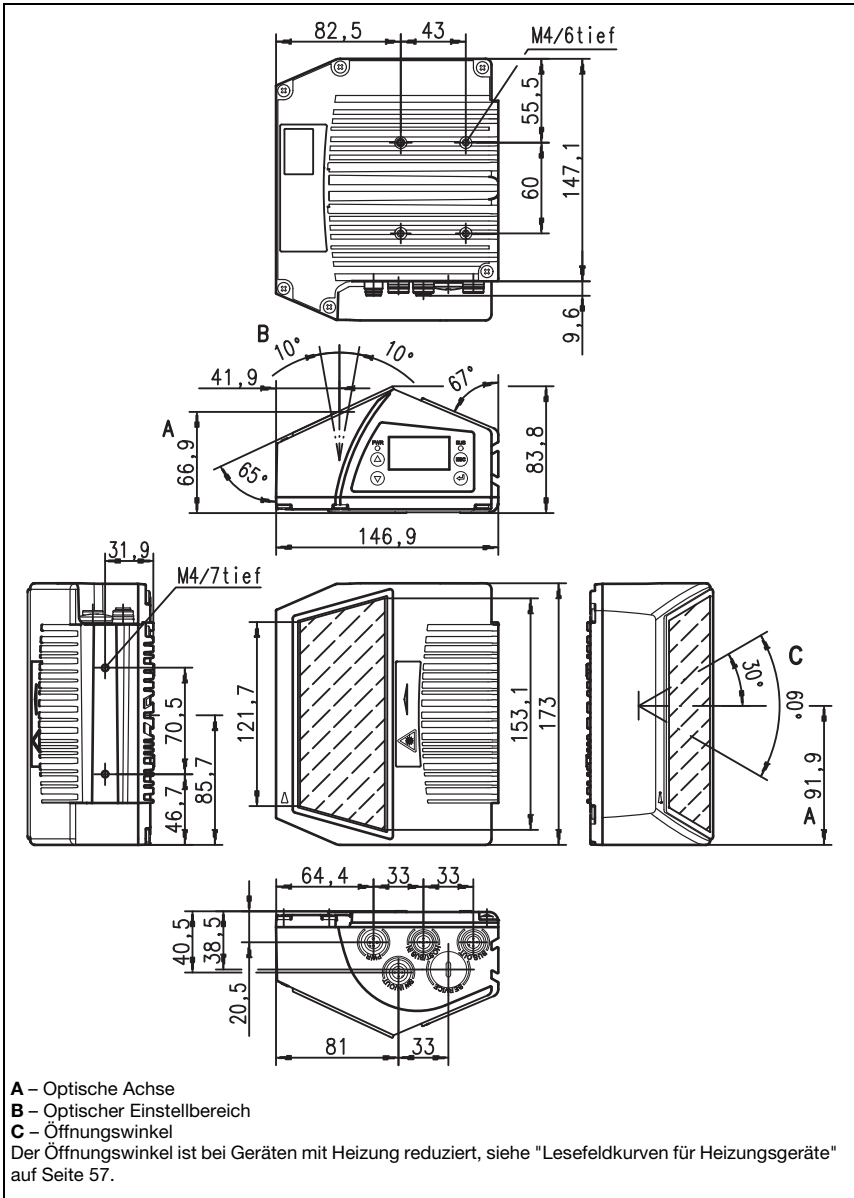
Maßzeichnung Scanner mit Umlenkspiegel BCL 548/i/S...100
